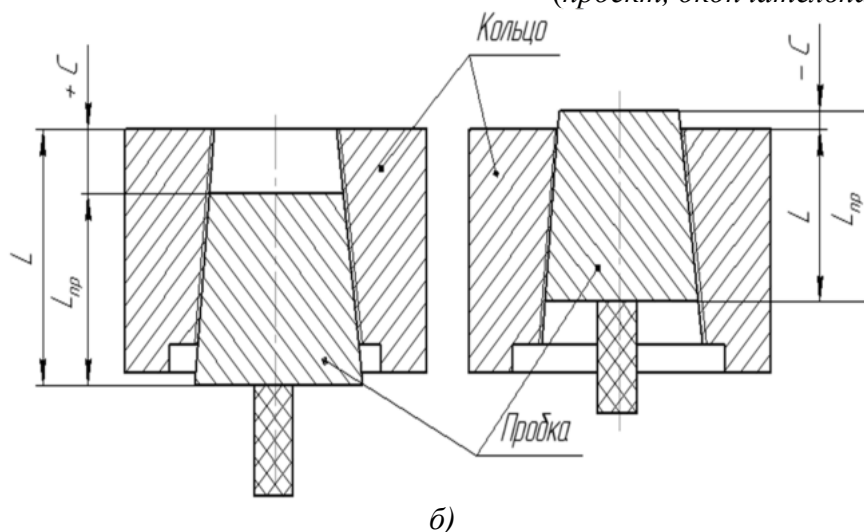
Схемы припасовки гладкого контрольного калибра-пробки и гладкого или резьбового рабочего калибра-кольца
